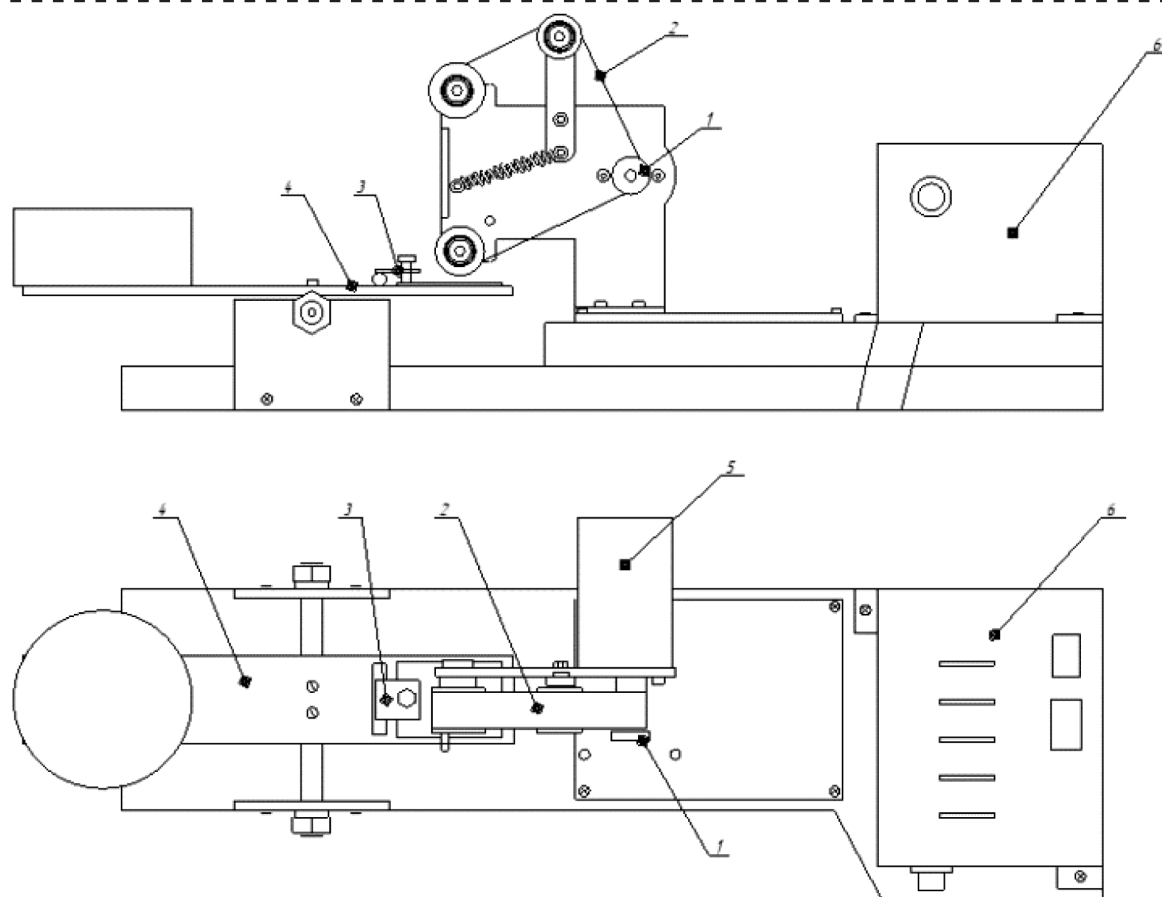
Схема установки ВИМ ЛТДП для сравнительных испытаний образцов на абразивную износостойкость: 1 — ротор с осью; 2 — абразивная лента; 3 — держатель образца; 4 — рычаг; 5 — электродвигатель; 6 — блок управления
